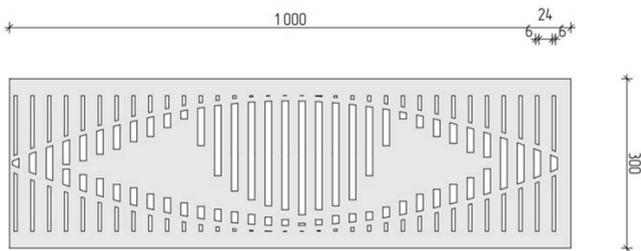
Чертеж схемы рисунка спинки стула «Мое отражение» для выполнения лазерной резки. Автор Ахметова Регина, группа ДИЗ6-2602а
